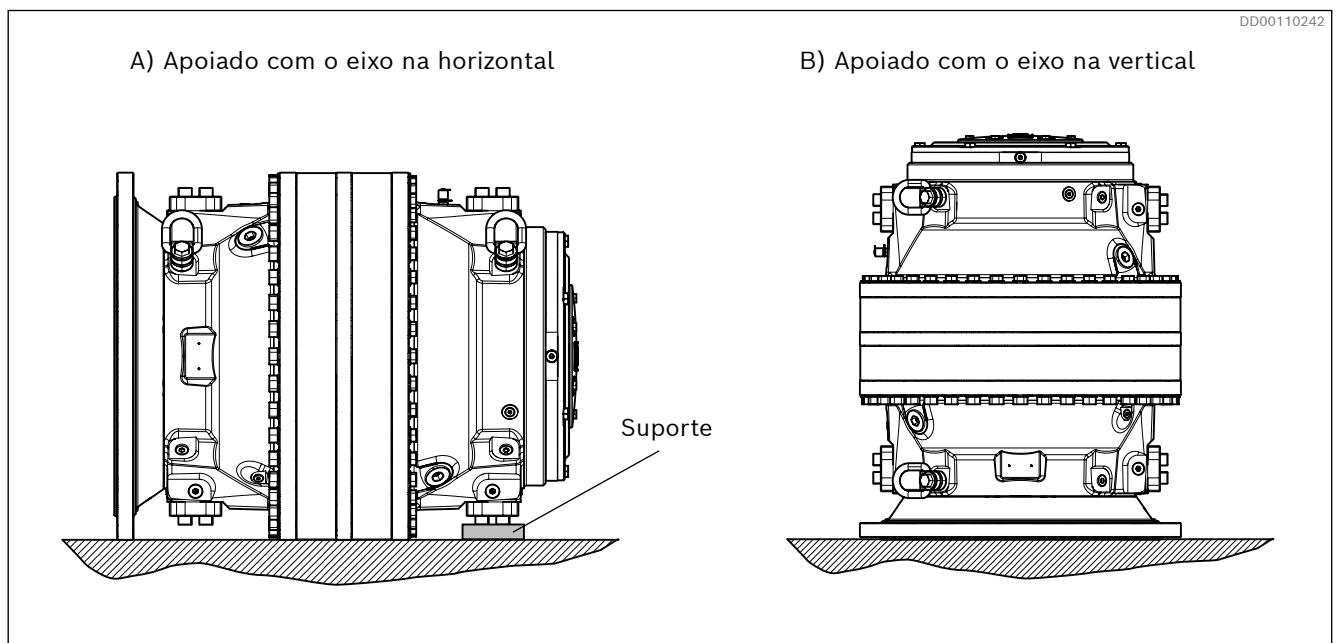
Exemplo, motor CBp apoiado em uma superfície plana
